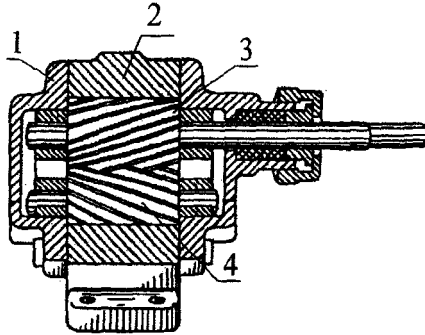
Шестеренный насос с косозубыми шестернями:
